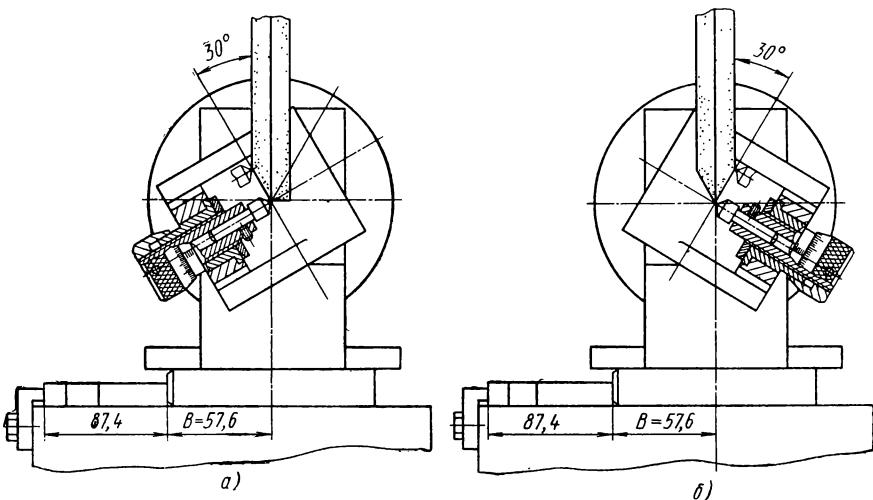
Схема заправки профиля круга для шлифования угловых направляющих:
